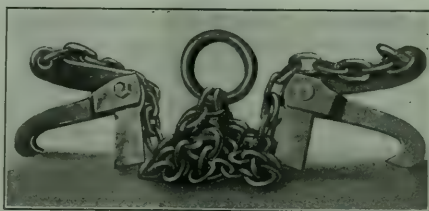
LOS GANCHOS PARA LAS LLANTAS
